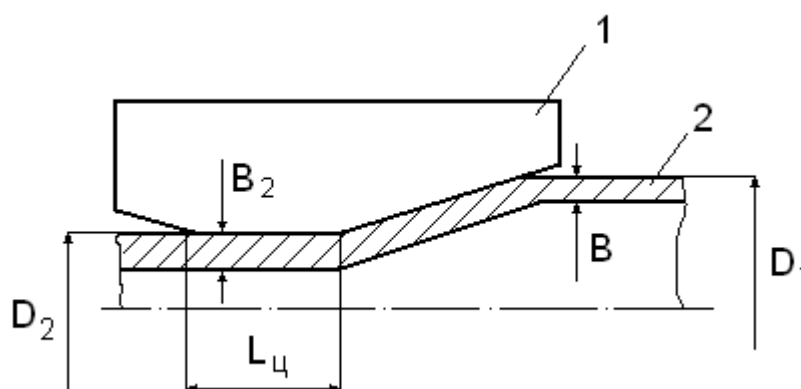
Розрахункова схема процесу ротаційного деформування
